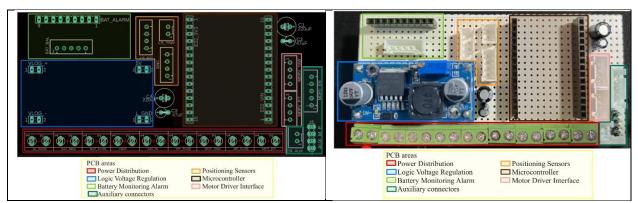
Zonas funcionales de la PCB diseñada (izquierda) y PCB manufacturada (derecha)
